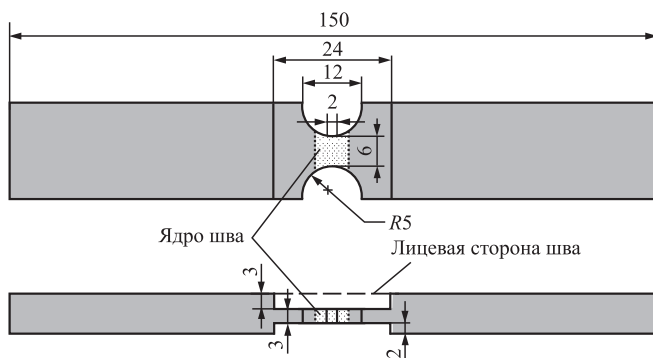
Схема вырезки образцов для испытаний на растяжение из металла ядра шва
